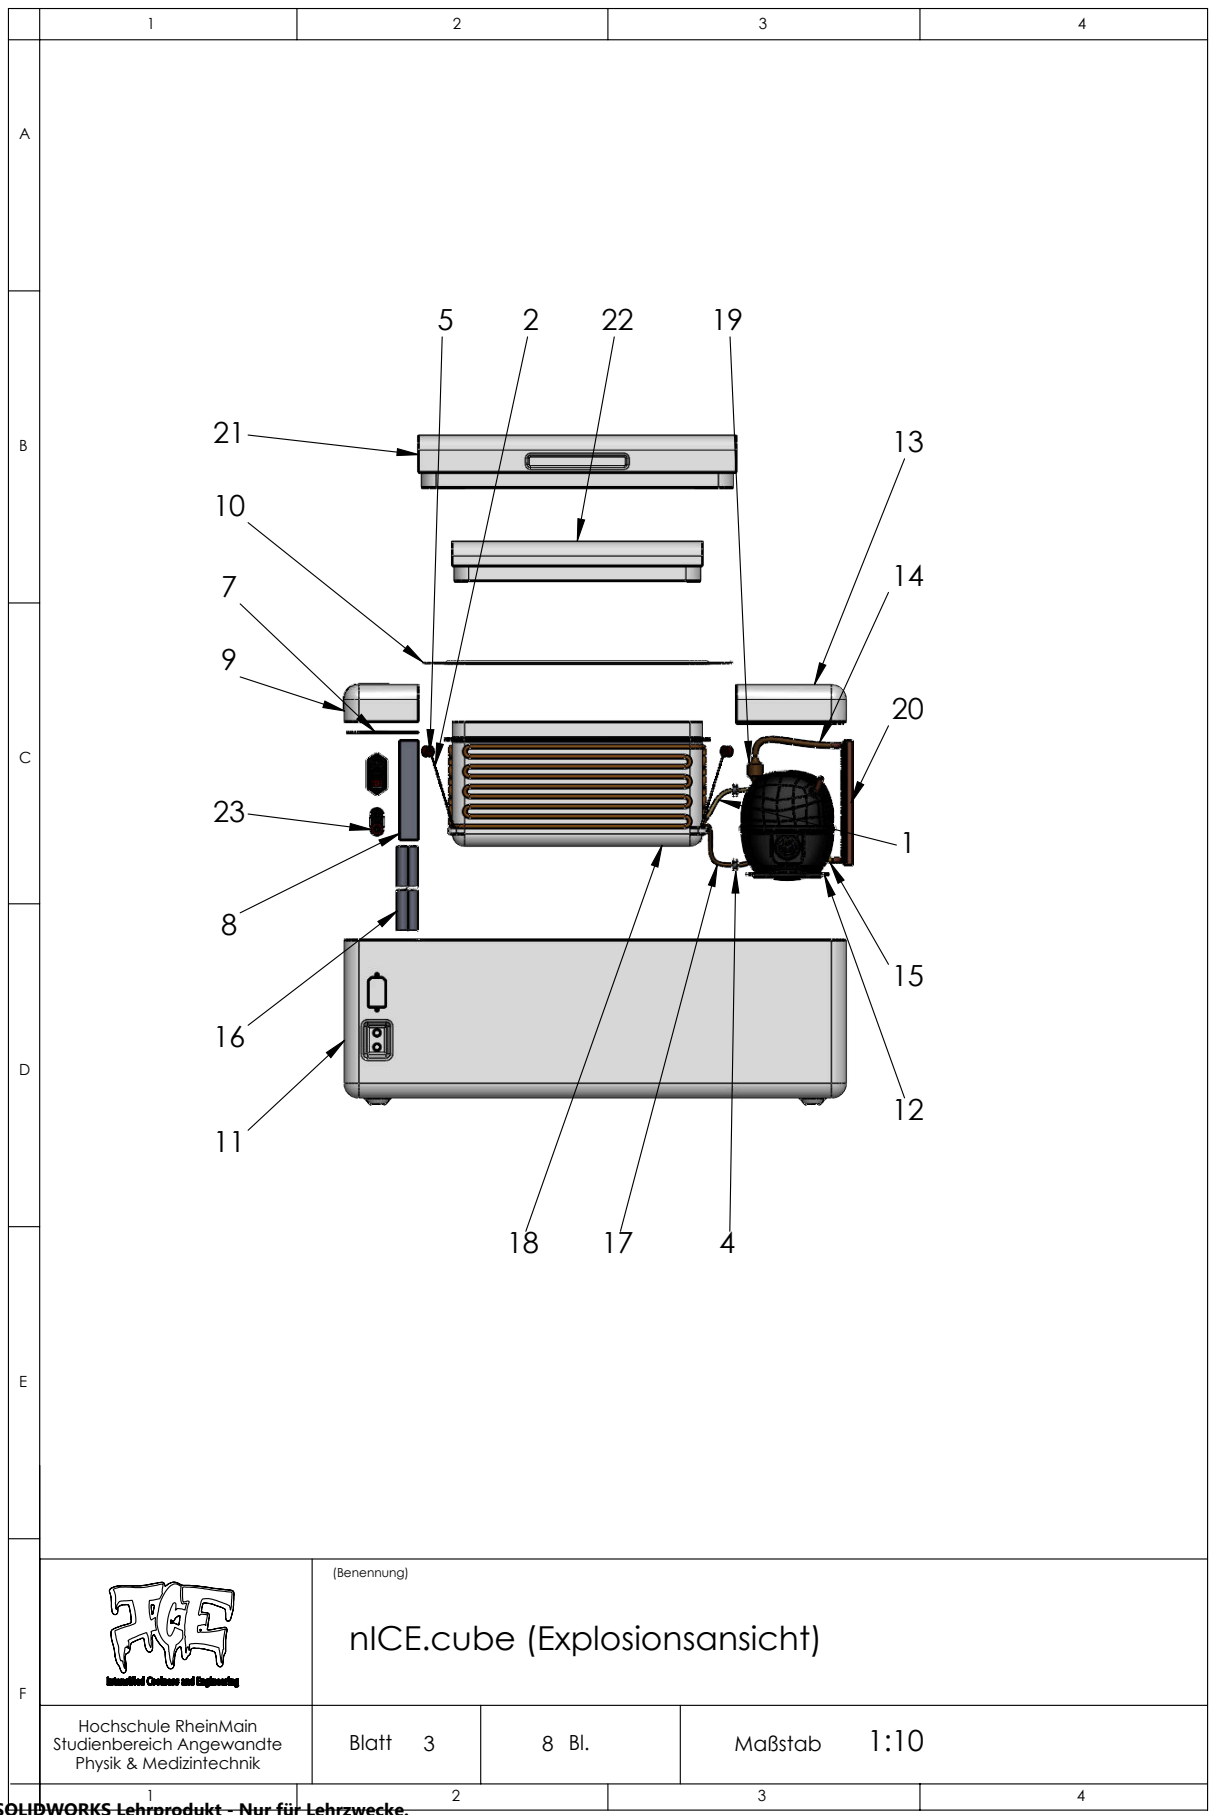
Explosionsansicht und Positionsnummern der Kernkomponenten.
